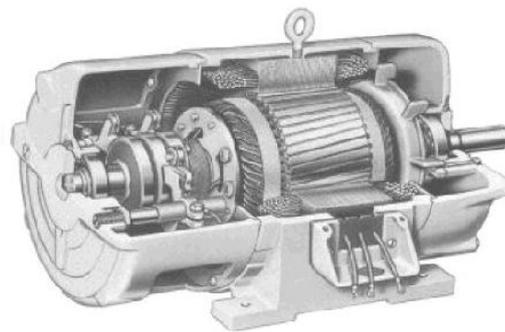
59 Motor trifásico asíncrono de rotor bobinado
